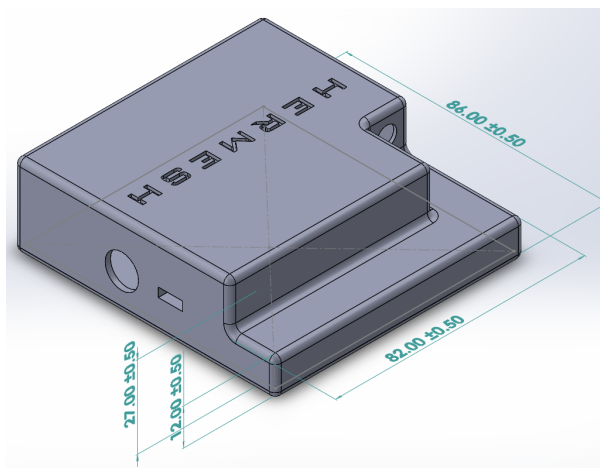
Diseño de carcasa en SolidWorks en vista isométrica.
